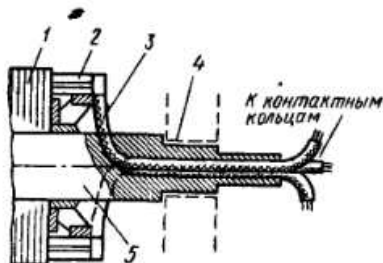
Соединение выводов фаз обмотки с контактными кольцами:
